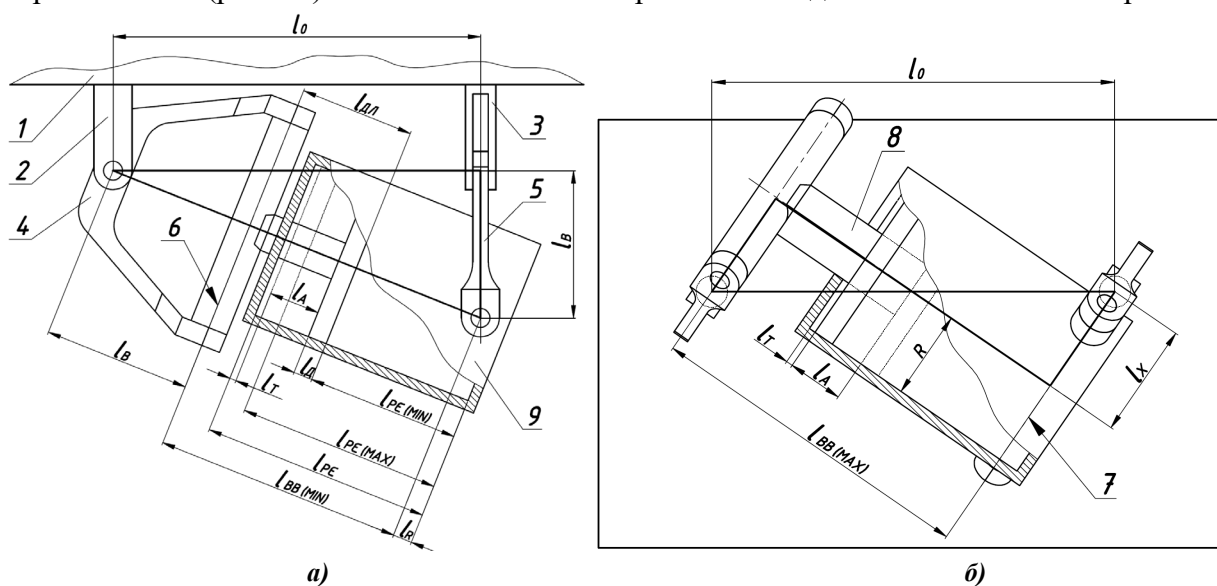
Розроблена машина для обробки деталей: а – вид зверху, б – вид спереду
